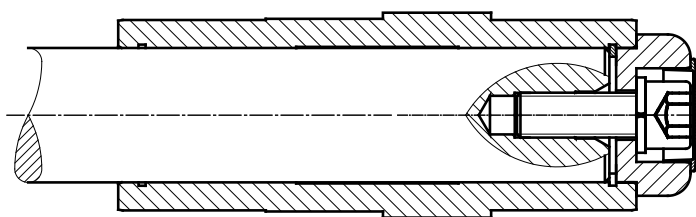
riduttore fissato ad un albero senza spallamento mediante elemento di fissaggio
